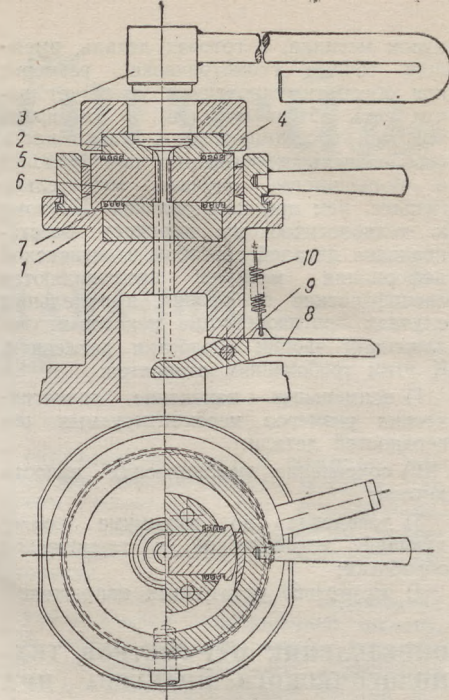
Штамп для осадки клапанов ГАЗ-ММ:
